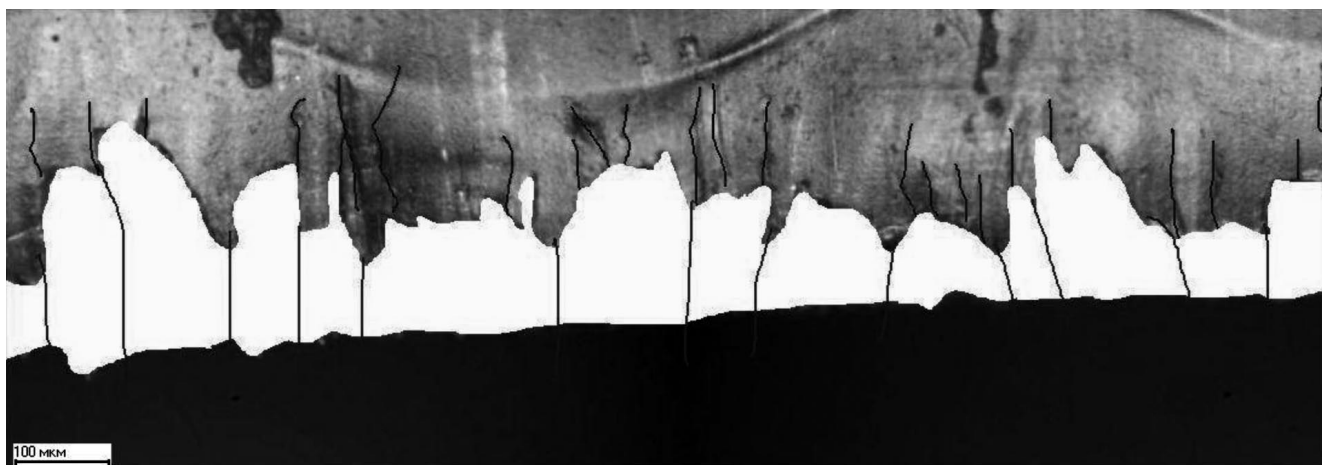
Фрагмент панорамного снимка поверхности реза образца из углепластика после операции резания на роботизированном фрезерном станке (образец Фр)
